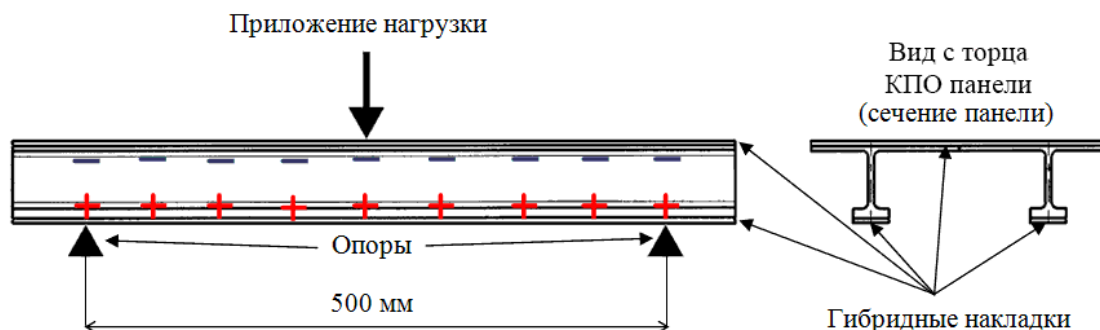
Схема нагружения КПО сварной гибридной панели крыла на трехточечный изгиб («+» – напряжения растяжения; «—» – напряжения сжатия)
